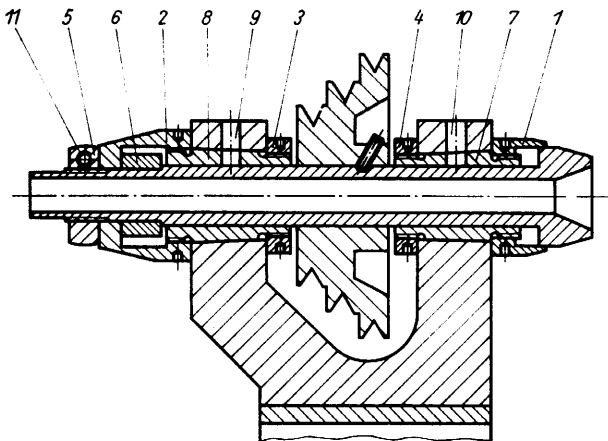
Spindelstock mit glatt zylindrischer Arbeitsspindel
